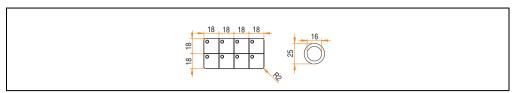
Tastenabmessungen - 5AC800.EXT3-00
